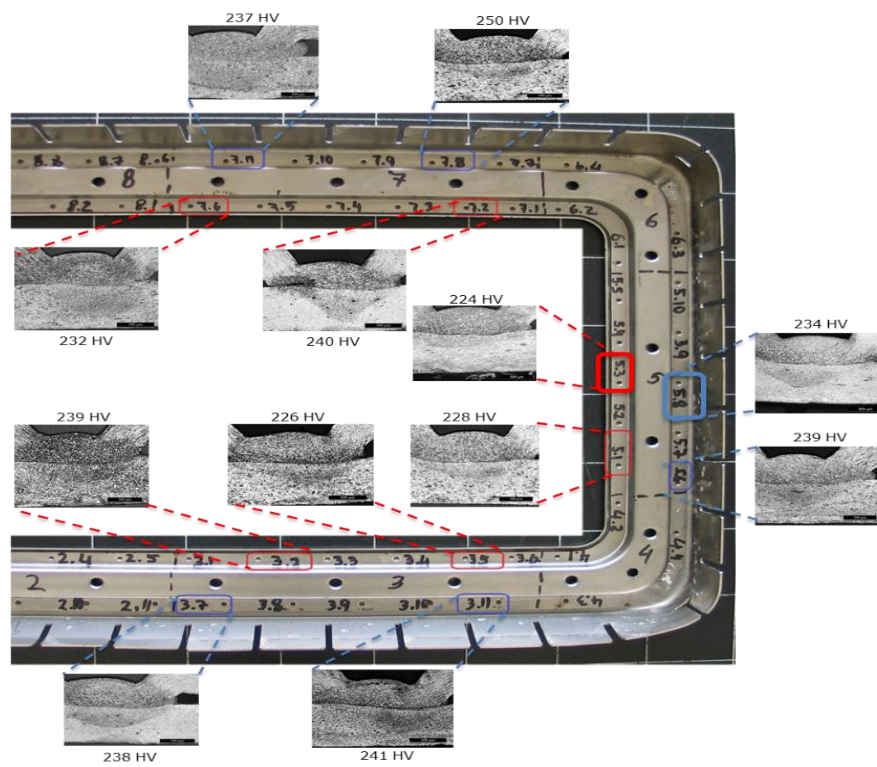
Mapa de soldaduras da peça F37/E20
